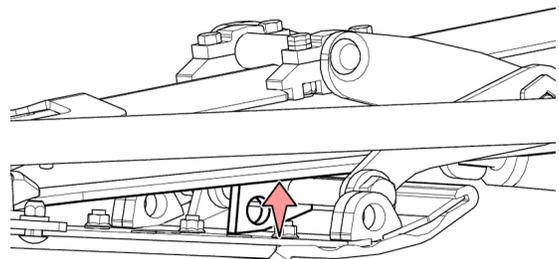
Точка контакта лопастного копирующего башмака привода
